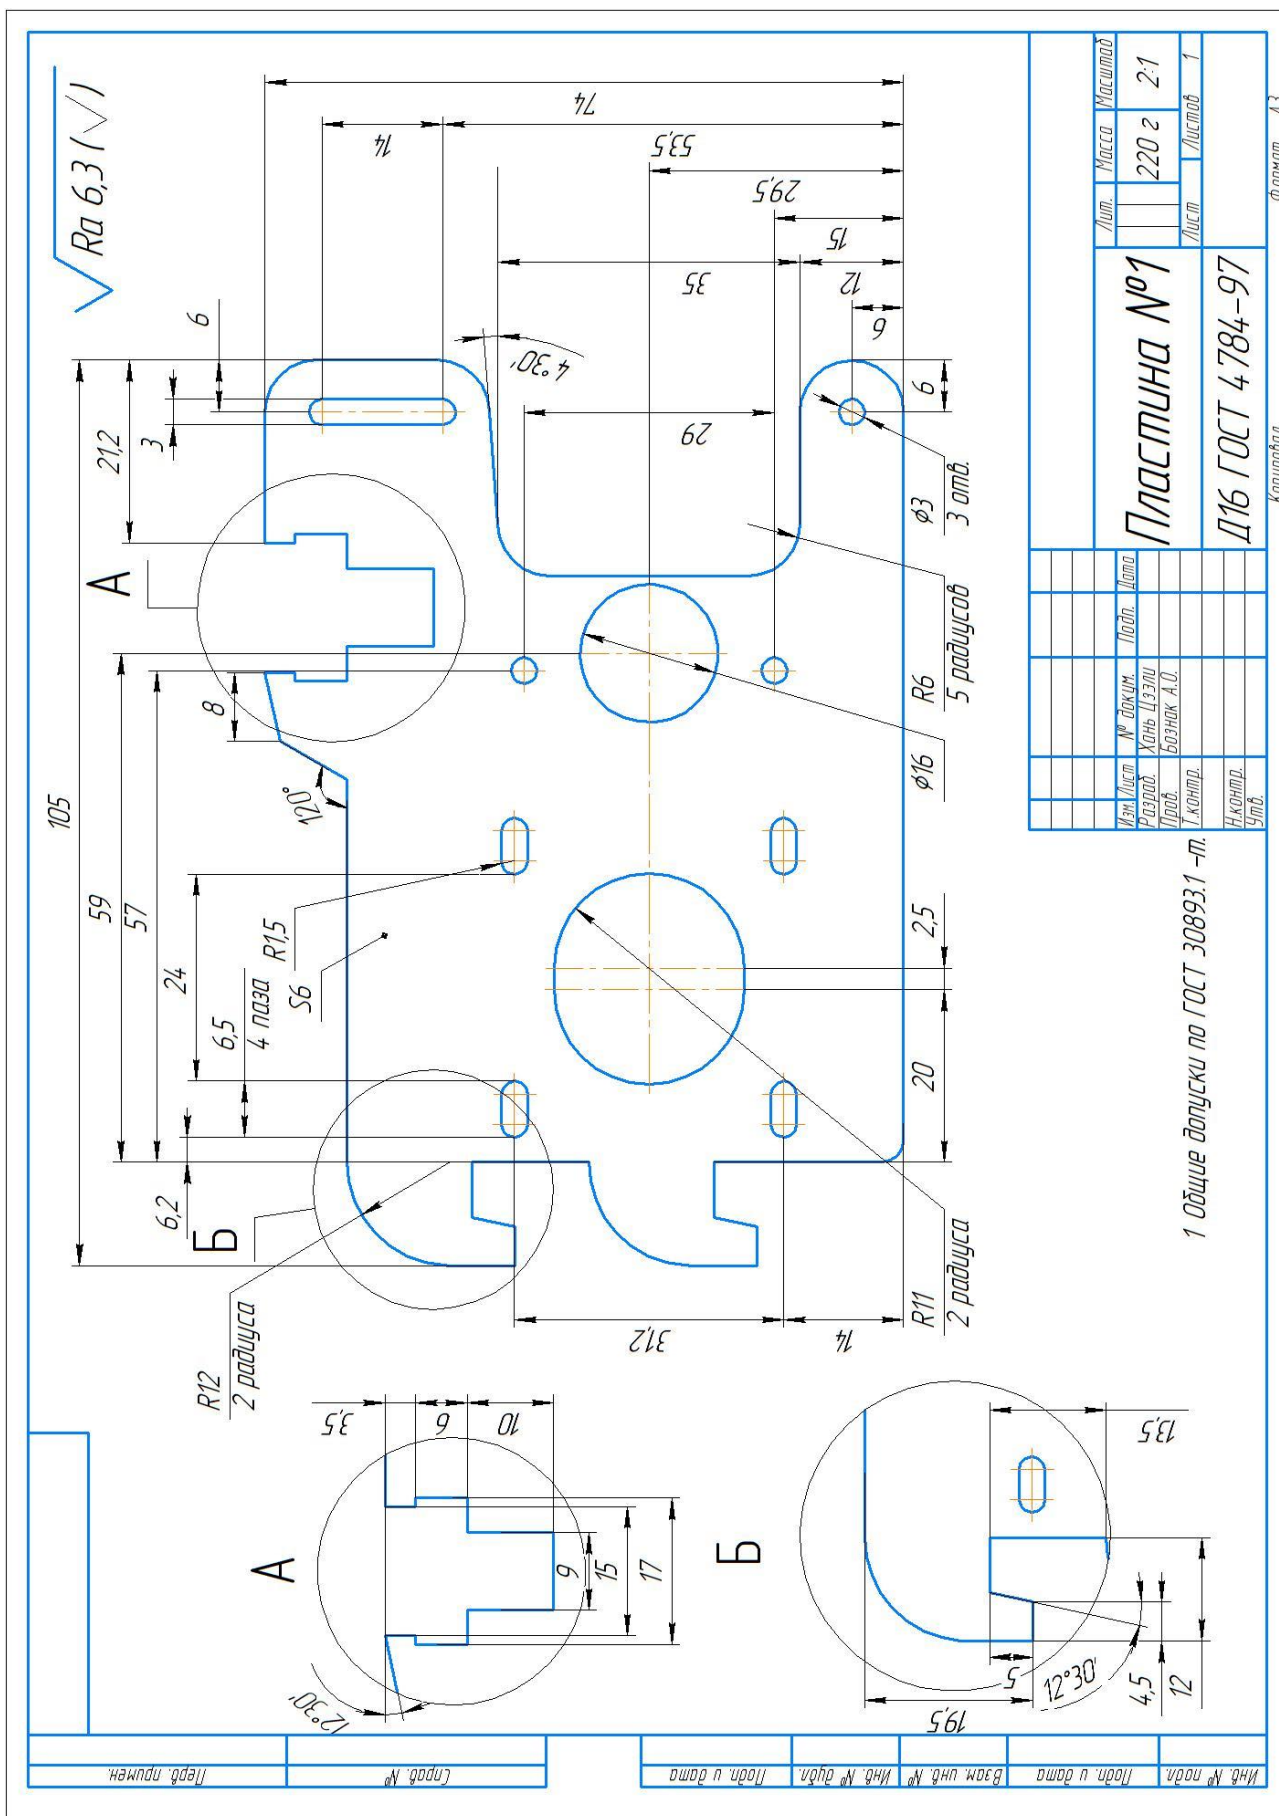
Чертеж детали «Пластина №1»
